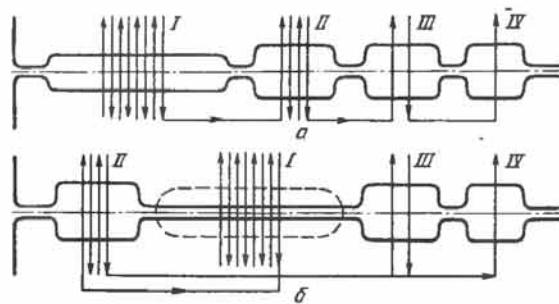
Калибровка валков блюминга с последовательным (а) и симметричным (б) расположением калибров (I—IV — номера калибров)
